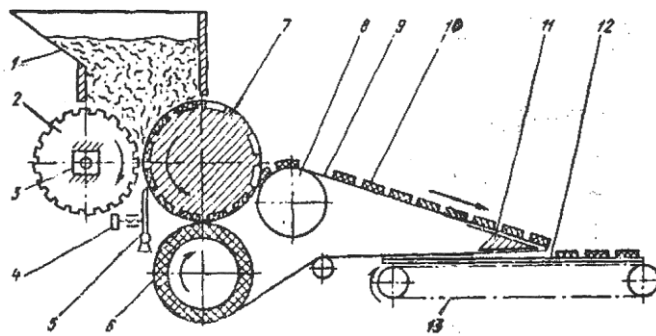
Схема ротаційної формуючої машини РМП: 1 – воронка; 2 – валок; 3 – підшипник; 4 – гвинт; 5 – ніж; 6 – барабан; 7 – ротор; 8 – ролик; 9 – стрічка; 10 – печиво; 11 – пластина-ніж; 12 – трафаретний лист; 13 – ланцюговий конвеєр.
